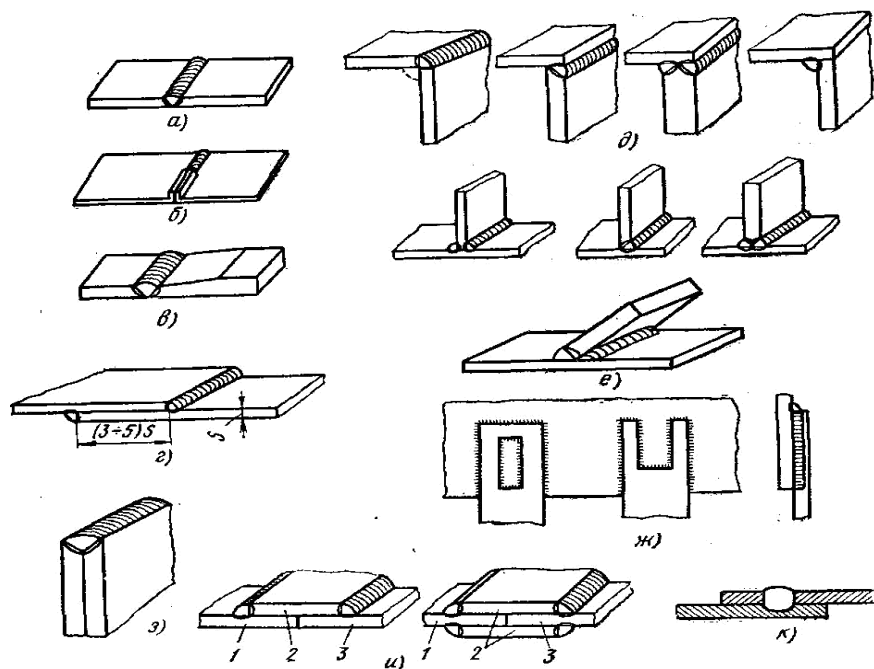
Основные виды сварных соединений:
